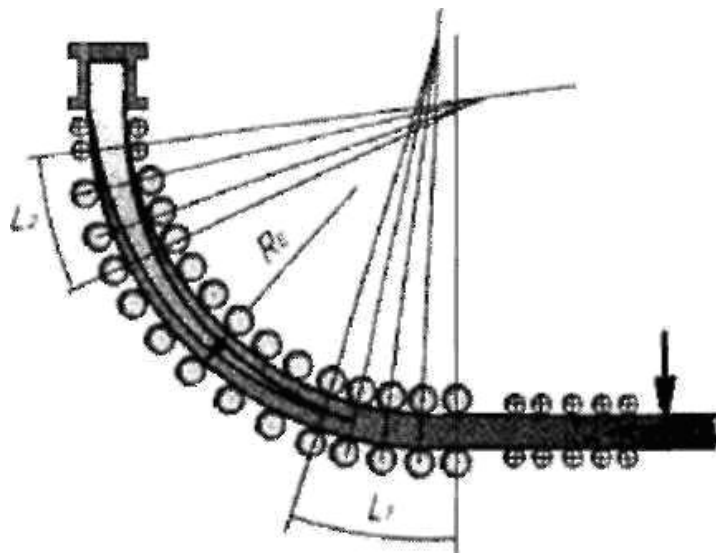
Схема МБЛЗ криволінійного типу (L_1 , L_2 – ділянки розгину і загину заготовки; R_0 – базовий радіус)
